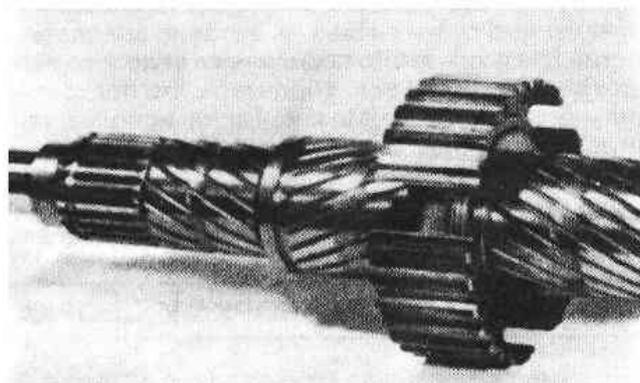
Ведомый вал коробки передач типа В и ступица синхронизатора 1/2 передачи (Разд.6)
